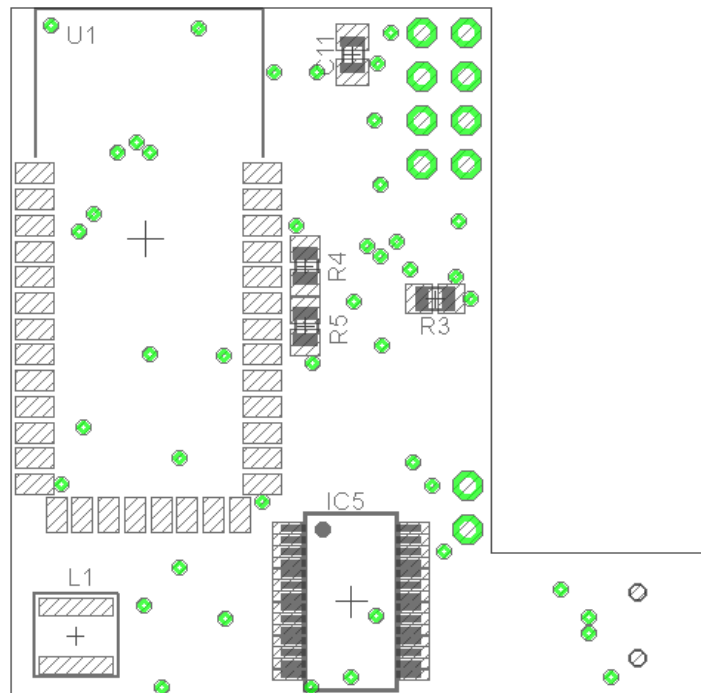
Bestückungsplan WristPCB gespiegelt Bottom
